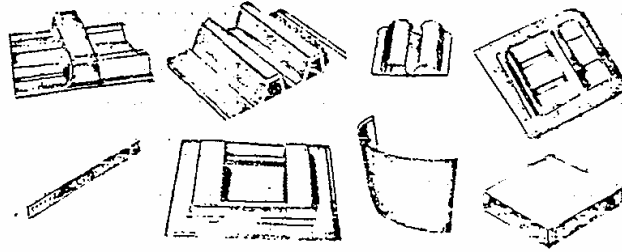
' de Tİ- ve Al- alaşımlarının süper plastik şekillendirilmesinde difüzyon kaynağı kullanılması görülmektedir.
